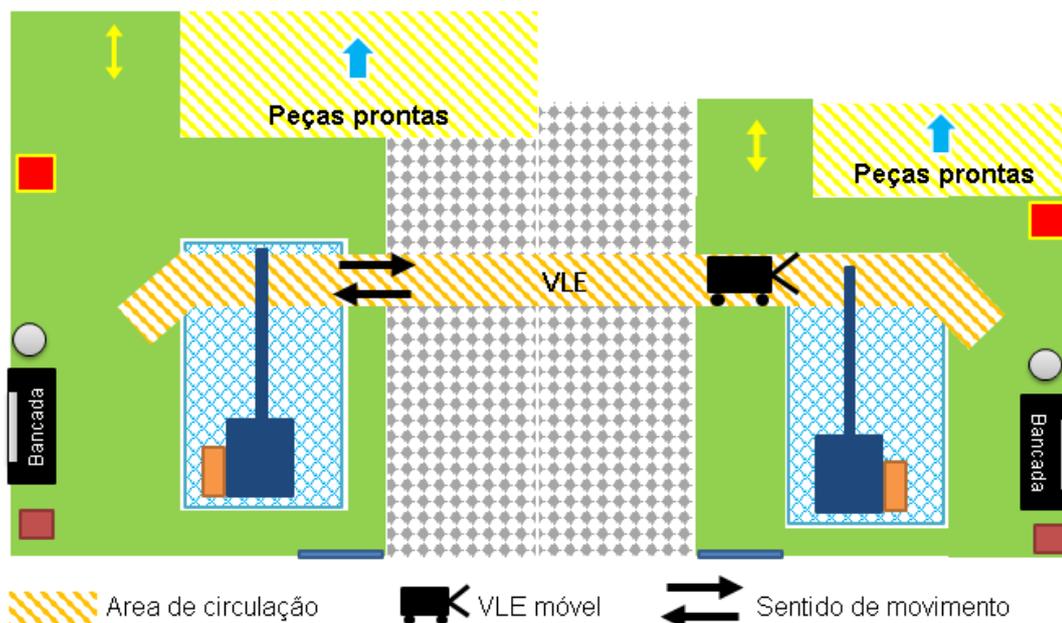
VLE móvel para soldagem - Technofiltro ecomático.
